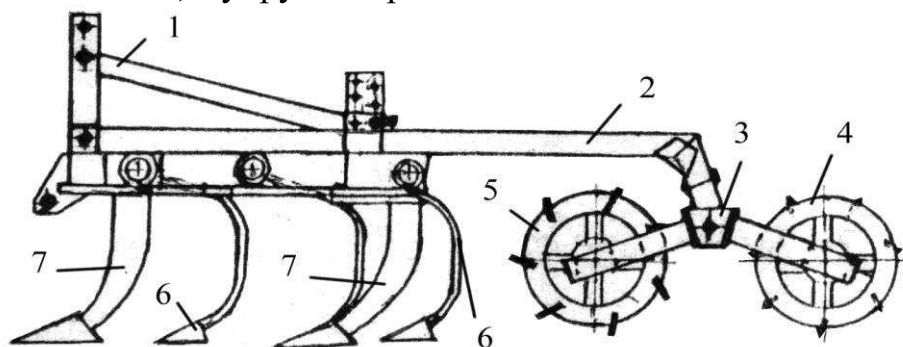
Комбинированный почвообрабатывающий агрегат АКР-3: 1 – навесная система; 2 – рама; 3 – балансир катков; 4 – прикатывающий каток; 5 – каток-разравниватель; 6 – упругая лапа стрельчатого типа; 7 – жесткая стойка
